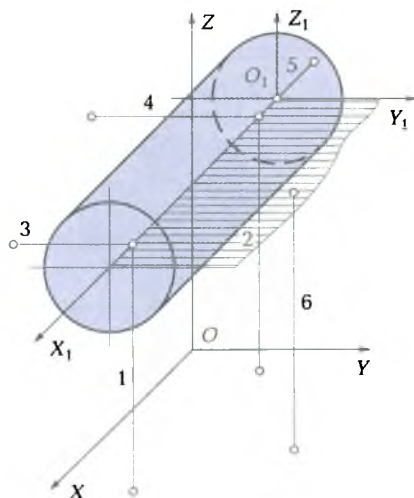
Наложение шести связей на цилиндрическую деталь
